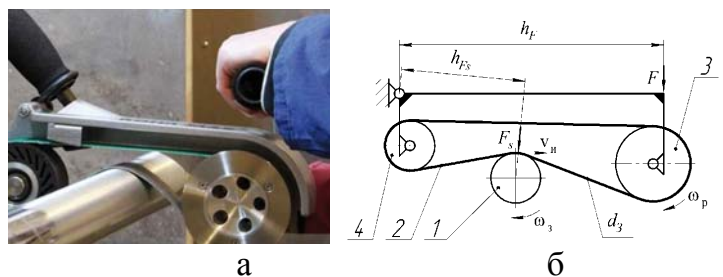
Дослідна установка: а – загальний вигляд; б – конструктивна схема: 1 – оброблювана заготовка; 2 – абразивна стрічка; 3 – ведучий ролик; 4 – натяжний ролик
